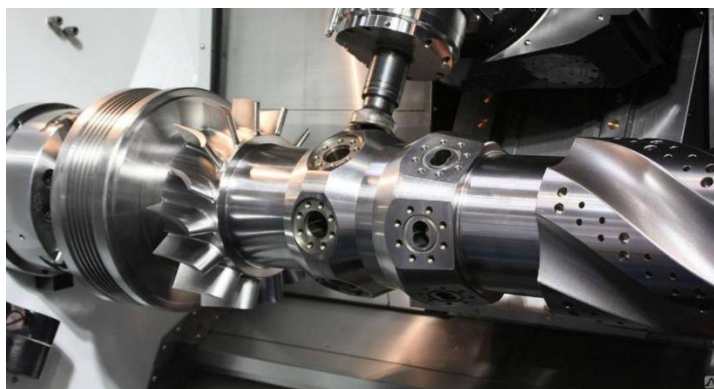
Обработка сложных металлических деталей на станках с ЧПУ
